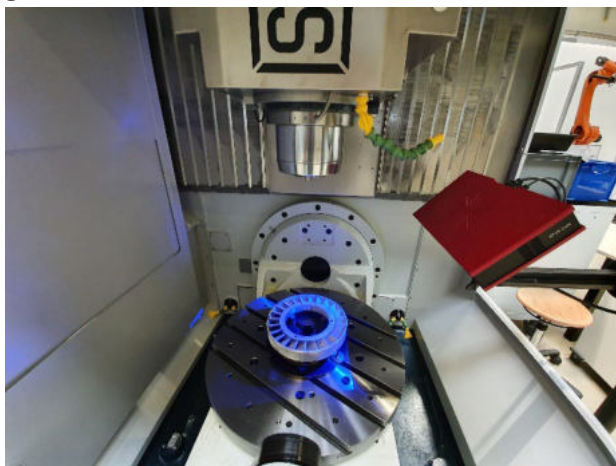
Optische Messung in der Einspannung der Werkzeugmaschine
